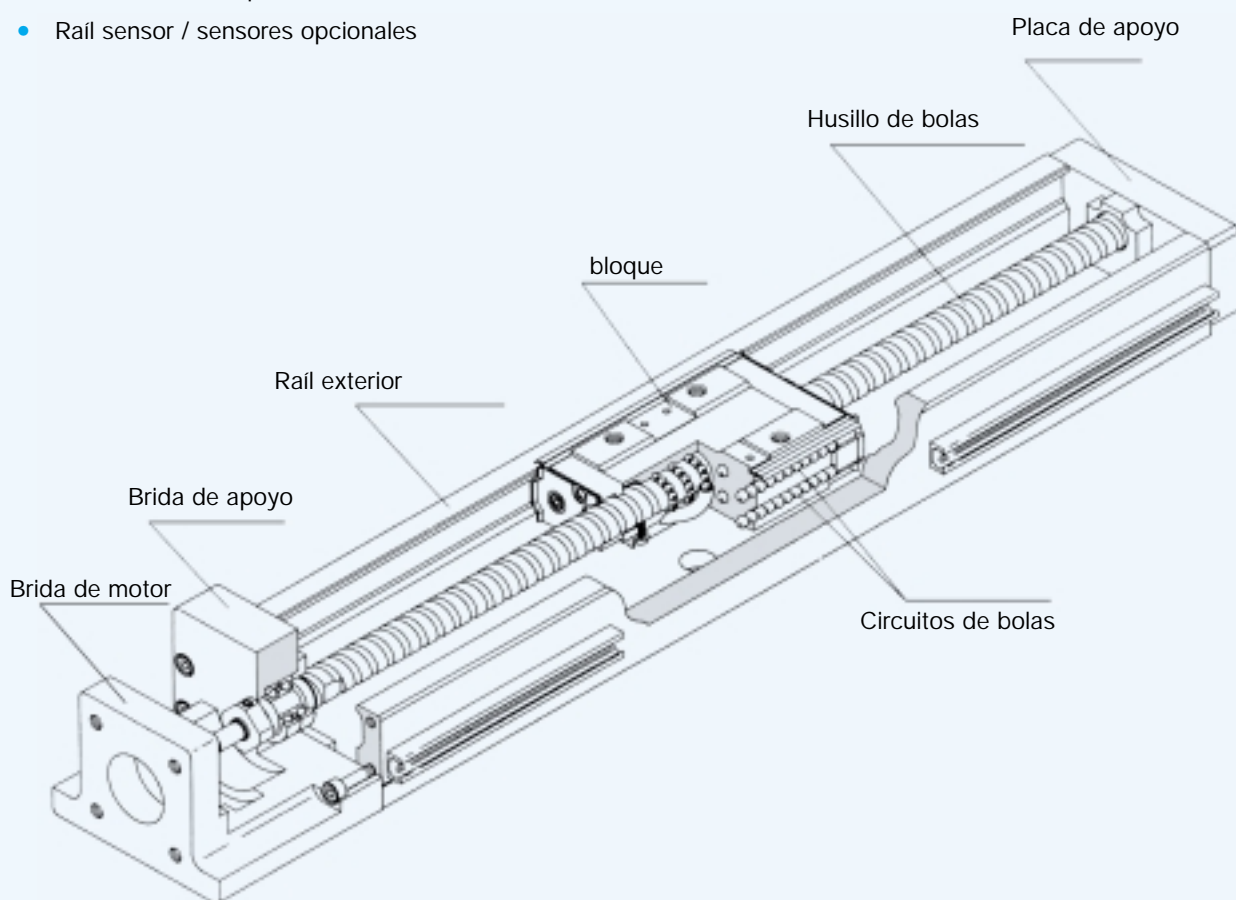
■ Corte transversal del módulo lineal compacto THK tipo KR.
